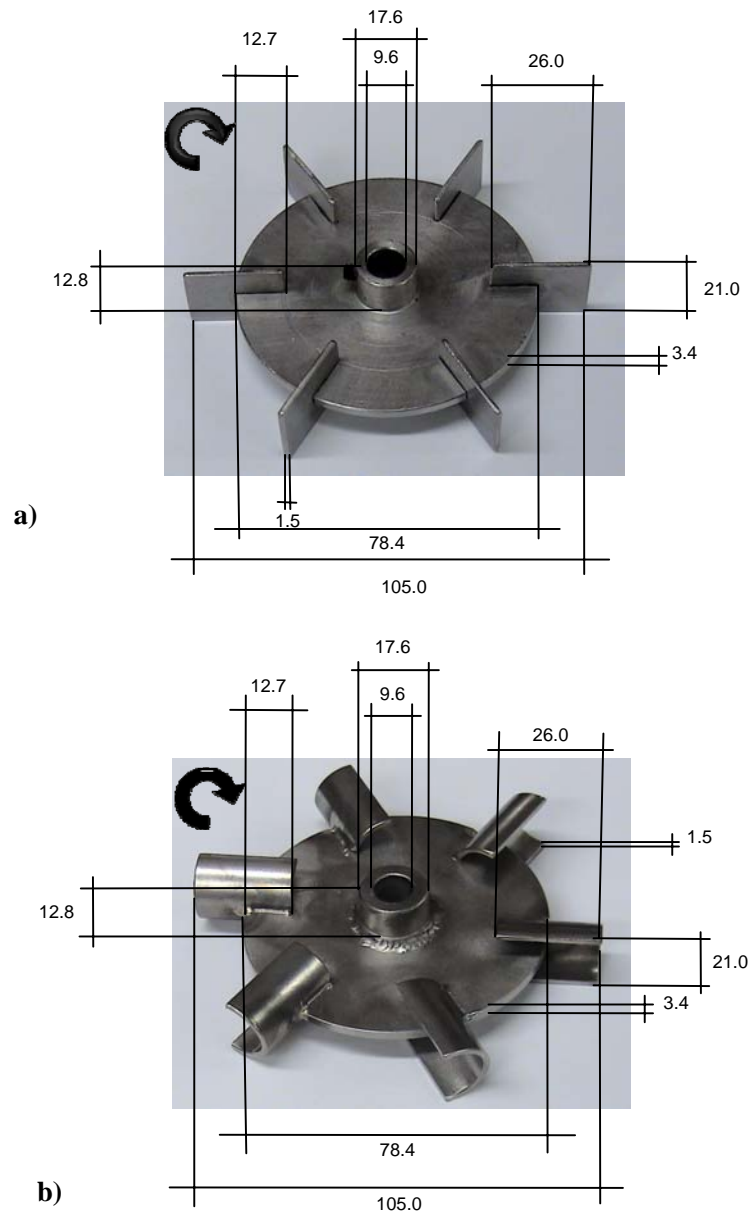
Dimensiones de los impulsores en mm: a) Turbina Rushton, b) Turbina “Smith”.
